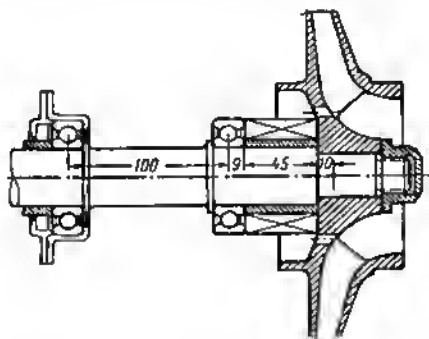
Disposición de los apoyos del árbol del rotor de álabes
